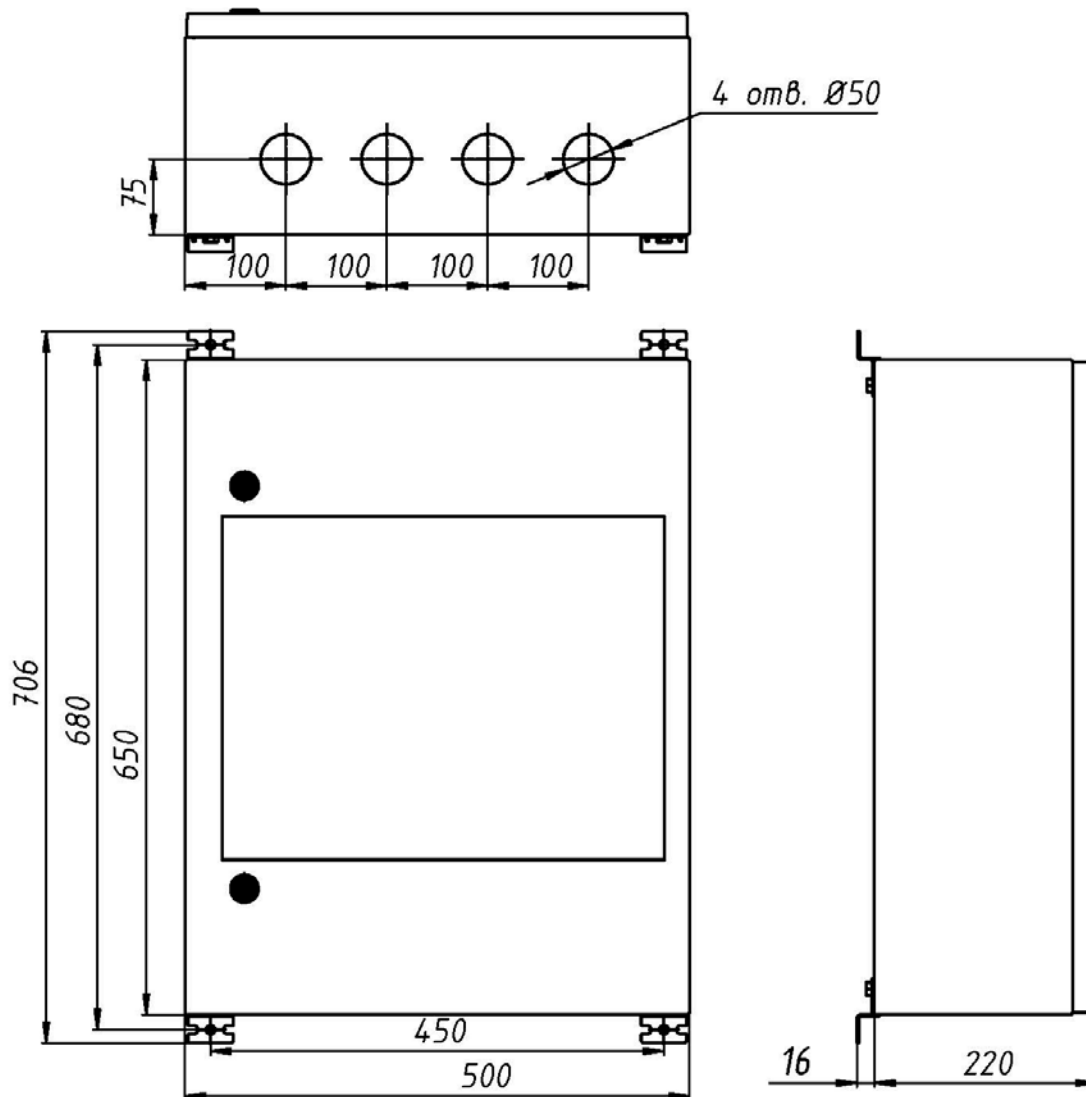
Габаритные размеры корпуса ППО КСПИ «Эгида»
